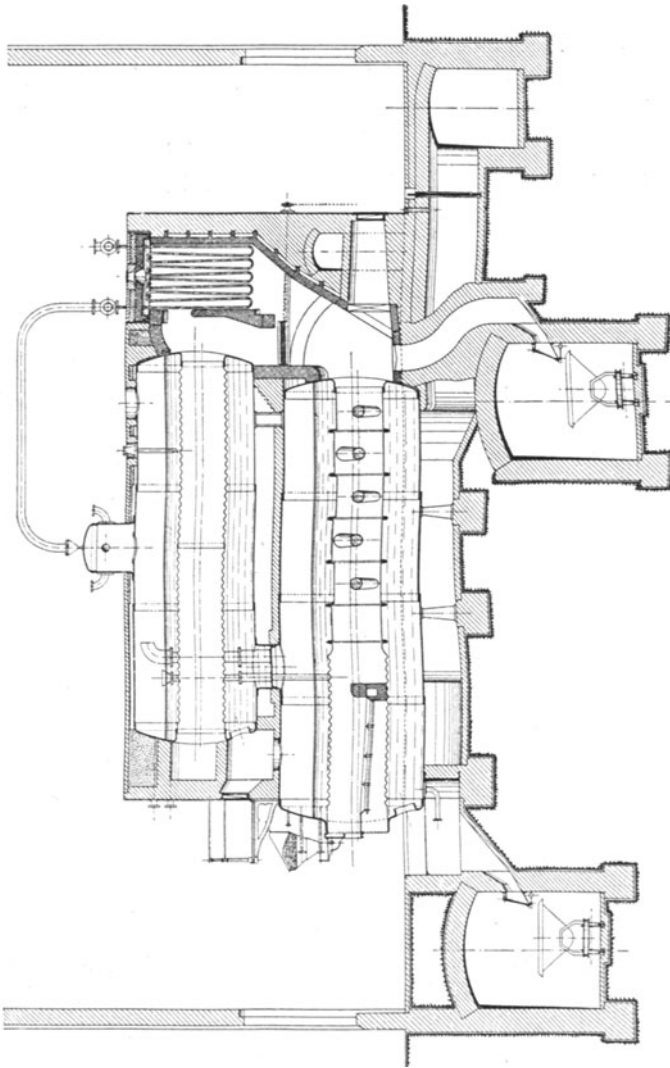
Kombiniertes Kessel der Firma F. & O. Schach, Meerane i. Sa., Kessel mit Gallowsrohr.
